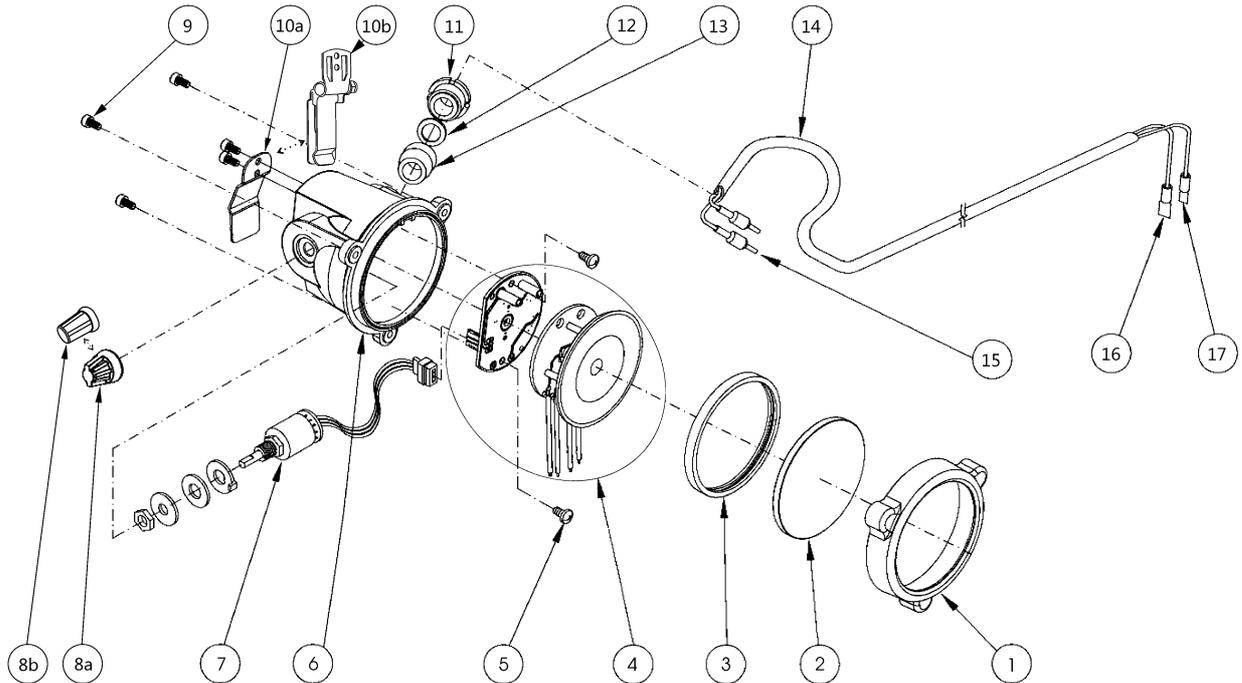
Explosionszeichnung des Eclipse Kopfstückes und Lampenkabels
